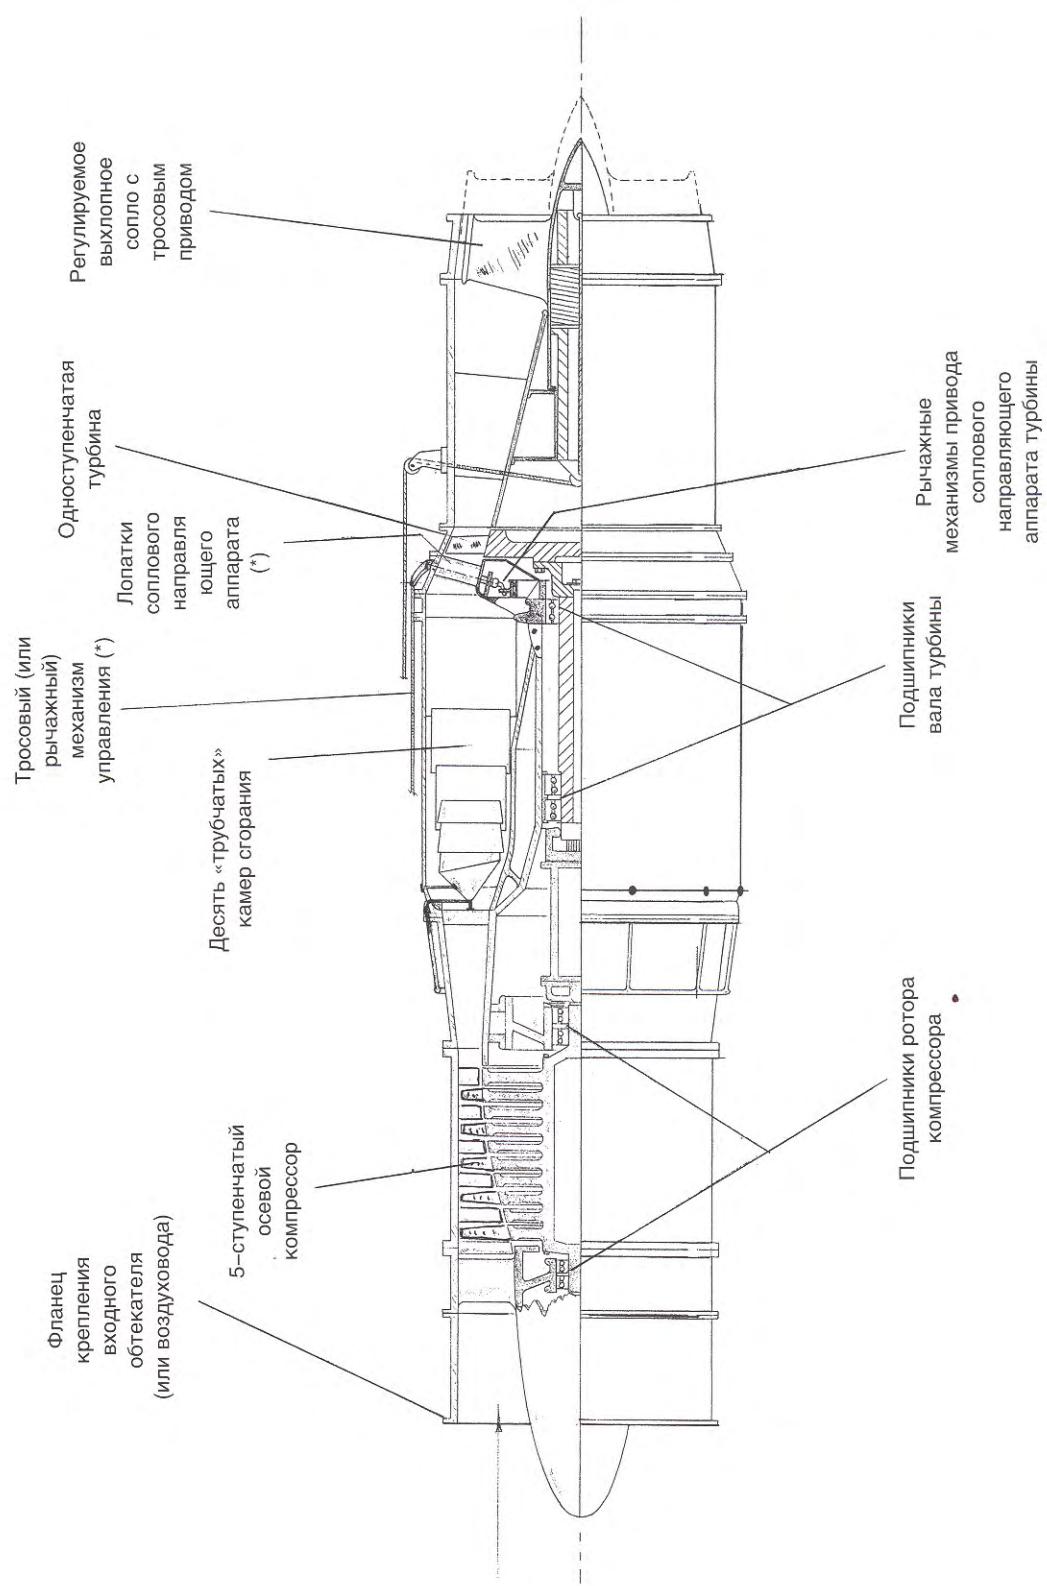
Турбореактивный двигатель HeS 30 (109-006) с осевым компрессором (схема выполнена автором)
